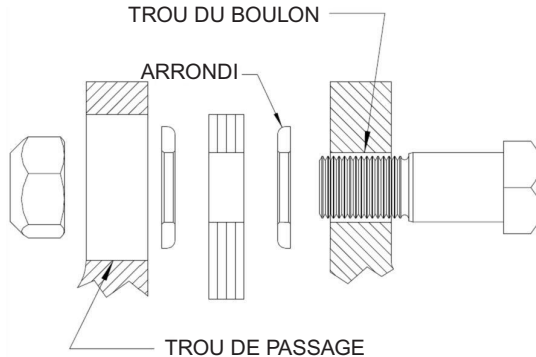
Boulon par le moyeu, les rondelles, l'écrou auto-freiné et l'assemblage du paquet des disques.
